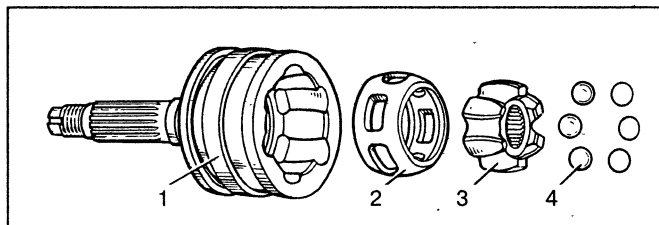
Детали наружного шарнира привода передних колес: 1 – корпус шарнира; 2 – сепаратор; 3 – обойма; 4 – шарик
